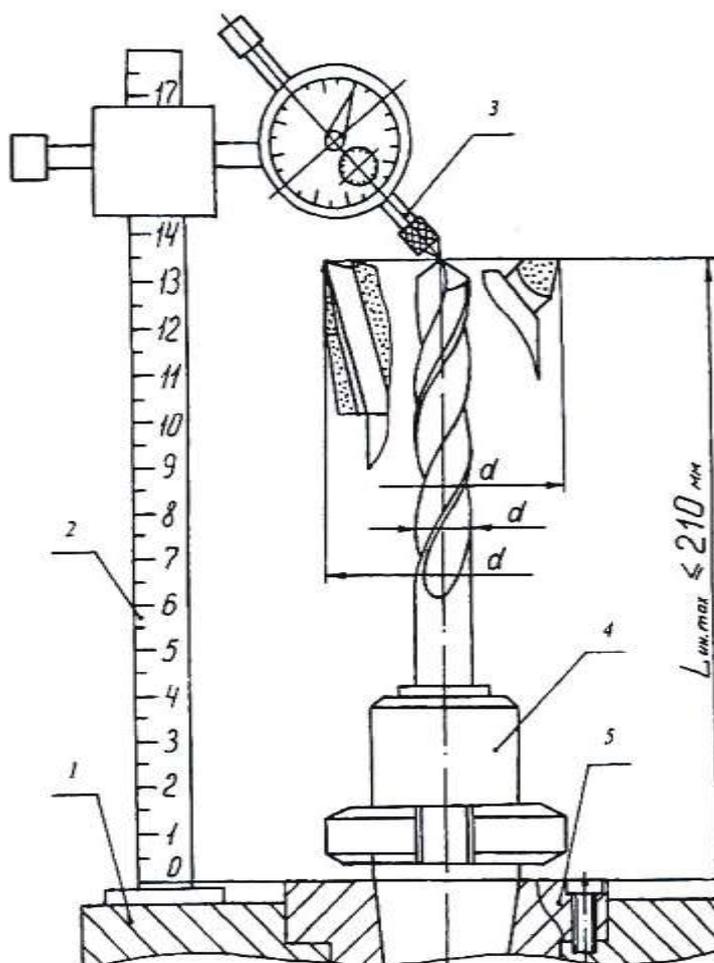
Приспособление для измерения наладочных размеров инструмента:
